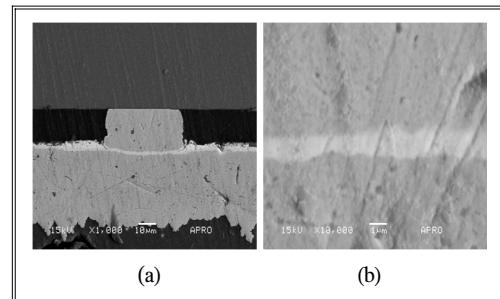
(a) 구리기둥과 PCB 기판간의 접합단면
